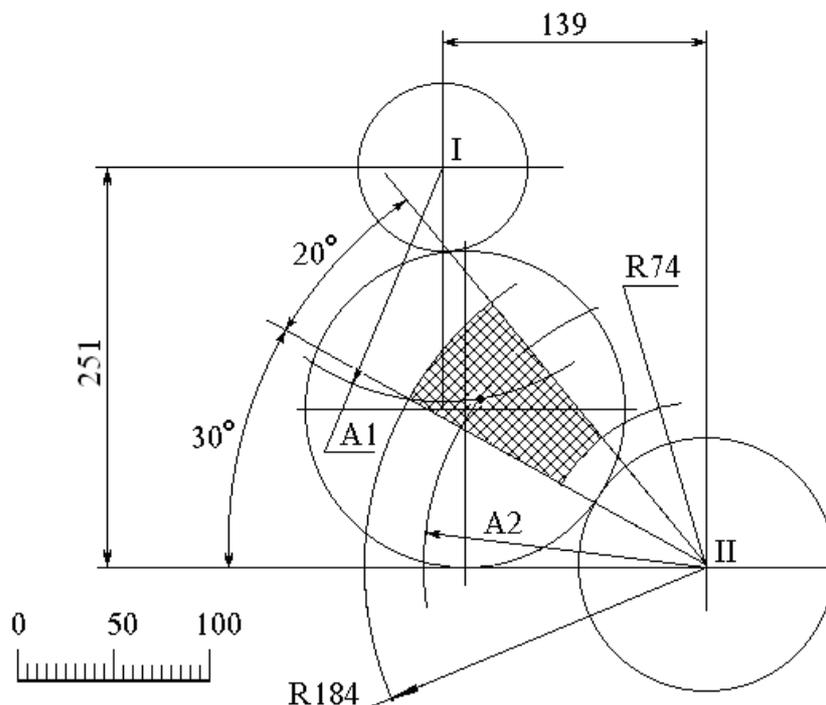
Чертеж для проверки возможности сцепления сменных шестерен
